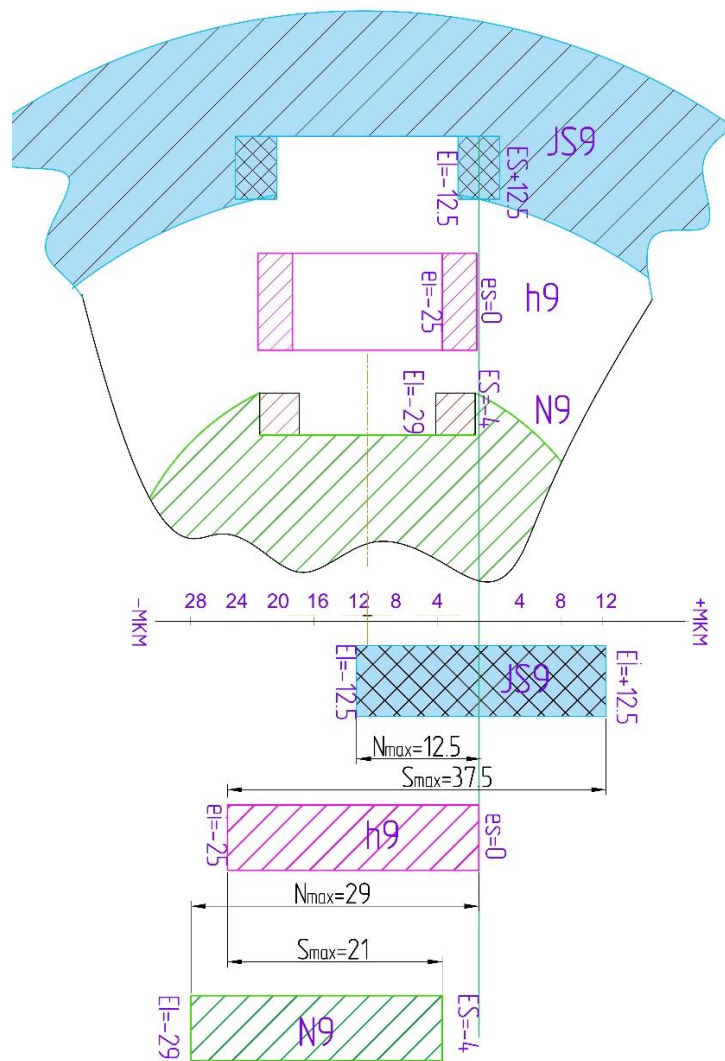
Схема розташування полів допусків для з'єднання
